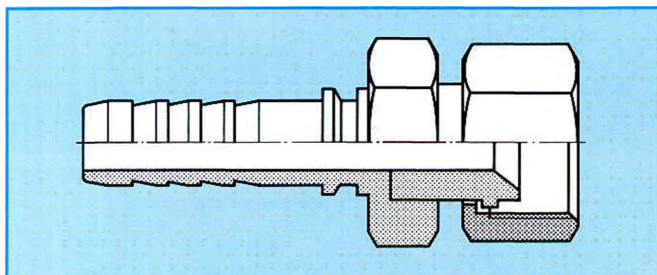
Прямой соединительный ниппель для резьбового соединения с уплотняющей отбортовкой
